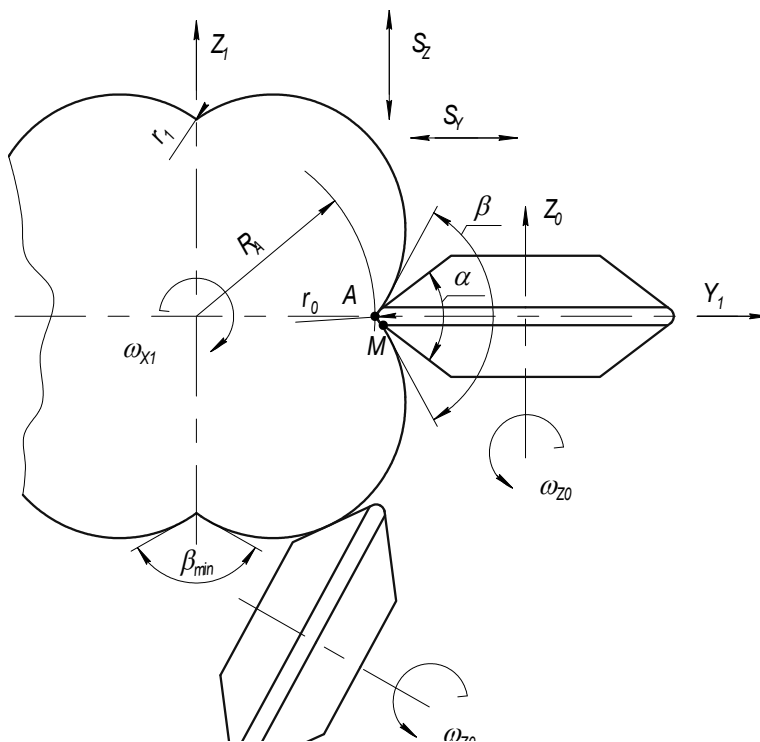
Схема обката сложного профиля детали инструментом с комбинированным профилем
